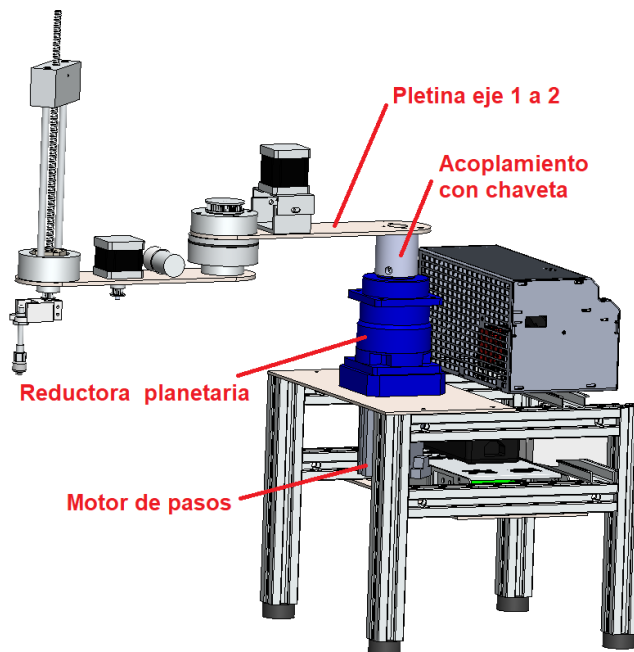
Montaje en solidworks del conjunto mecánicos del eje 1
